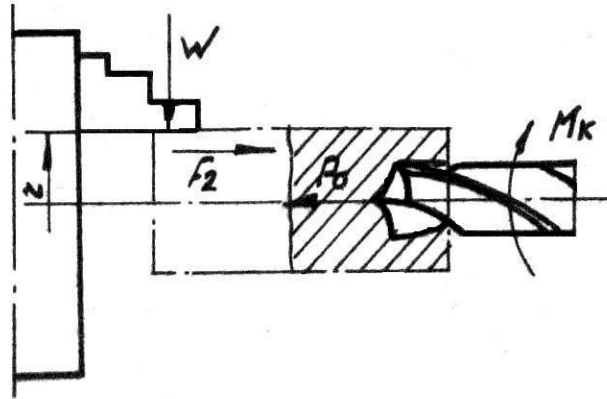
Схема установки при свердленні отвору в заготовці, яка закріплена в трьохкулачковому патроні
